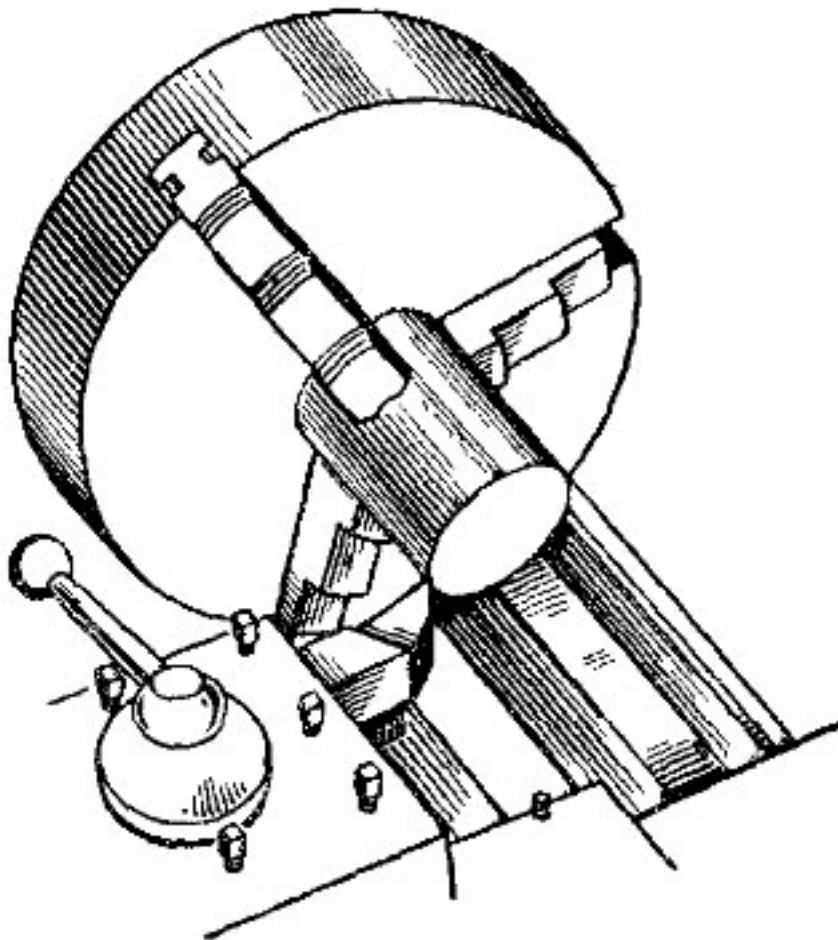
Закрепление короткой круглой детали в самоцентрирующем патроне при подрезании торца
